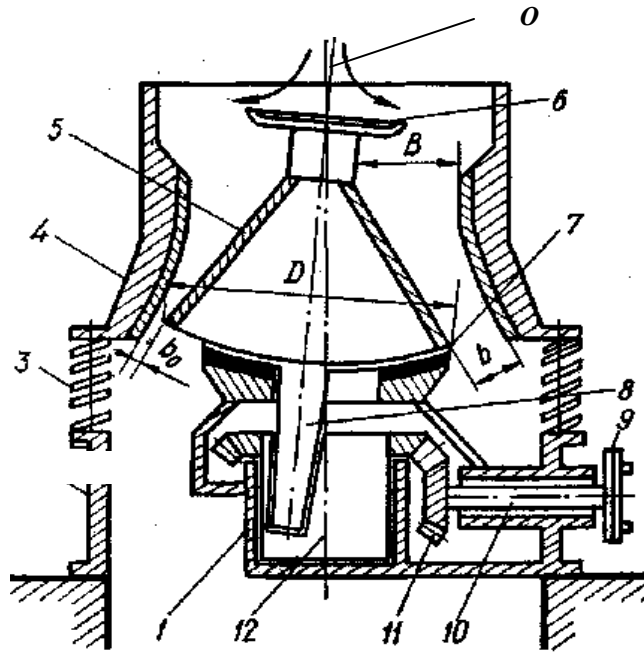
Принципиальная схема конусной дробилки для среднего и мелкого дробления: 1 – эксцентриковый стакан; 2 – корпус дробилки (станина); 3 – пружина с болтом; 4 – неподвижная коническая чаша; 5 – подвижный (дробящий конус); 6 – распределительная тарелка; 7 – подпятник; 8 – вал; 9 – муфта; 10 – приводной вал; 11 – коническая зубчатая передача; 12 – ось эксцентрикового стакана
